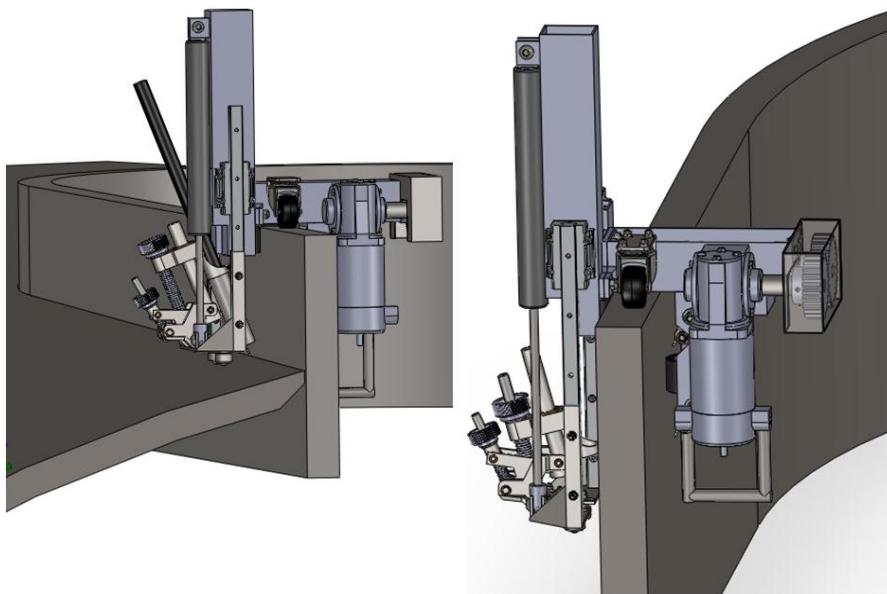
Dispositivo de soldadura colocado no aro da porta
